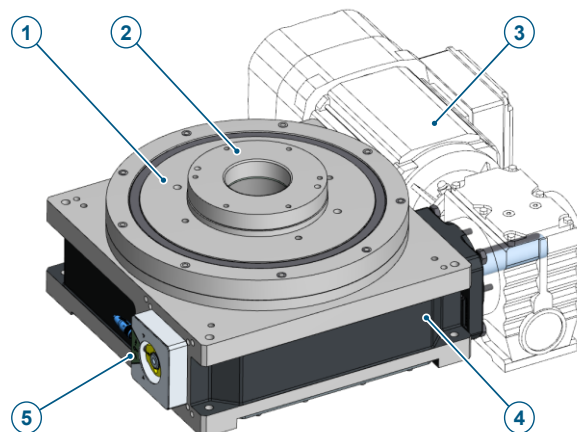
Aufbau Trommelkurvenrundtisch – Distanzausführung geschlossene Beschaltung
